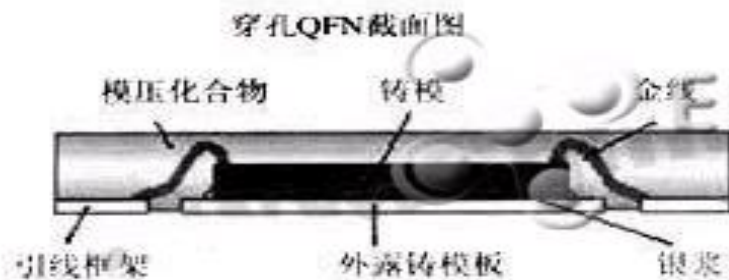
采用PCB焊接的外露散热焊盘的QFN封装
